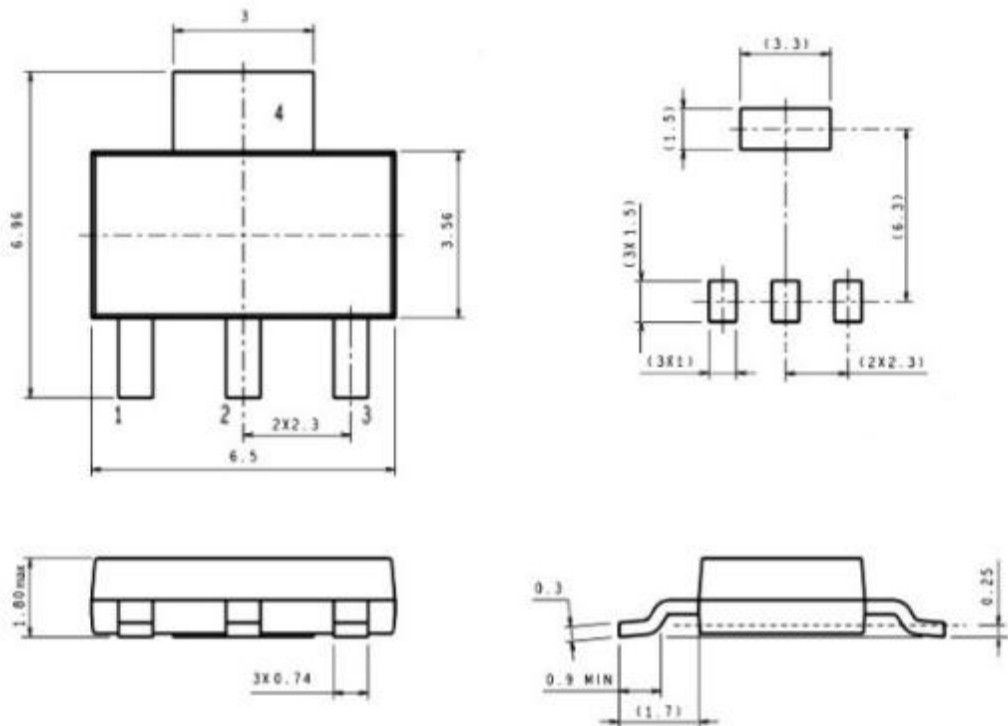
Габаритні розміри стабілізатора L7805
